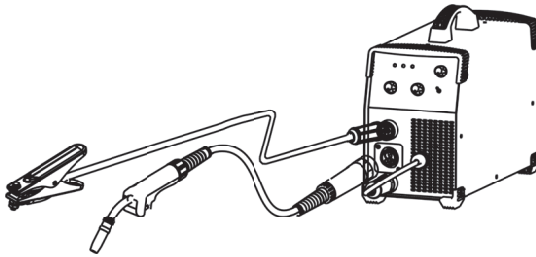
Схема подключения для сварки в среде защитных газов
